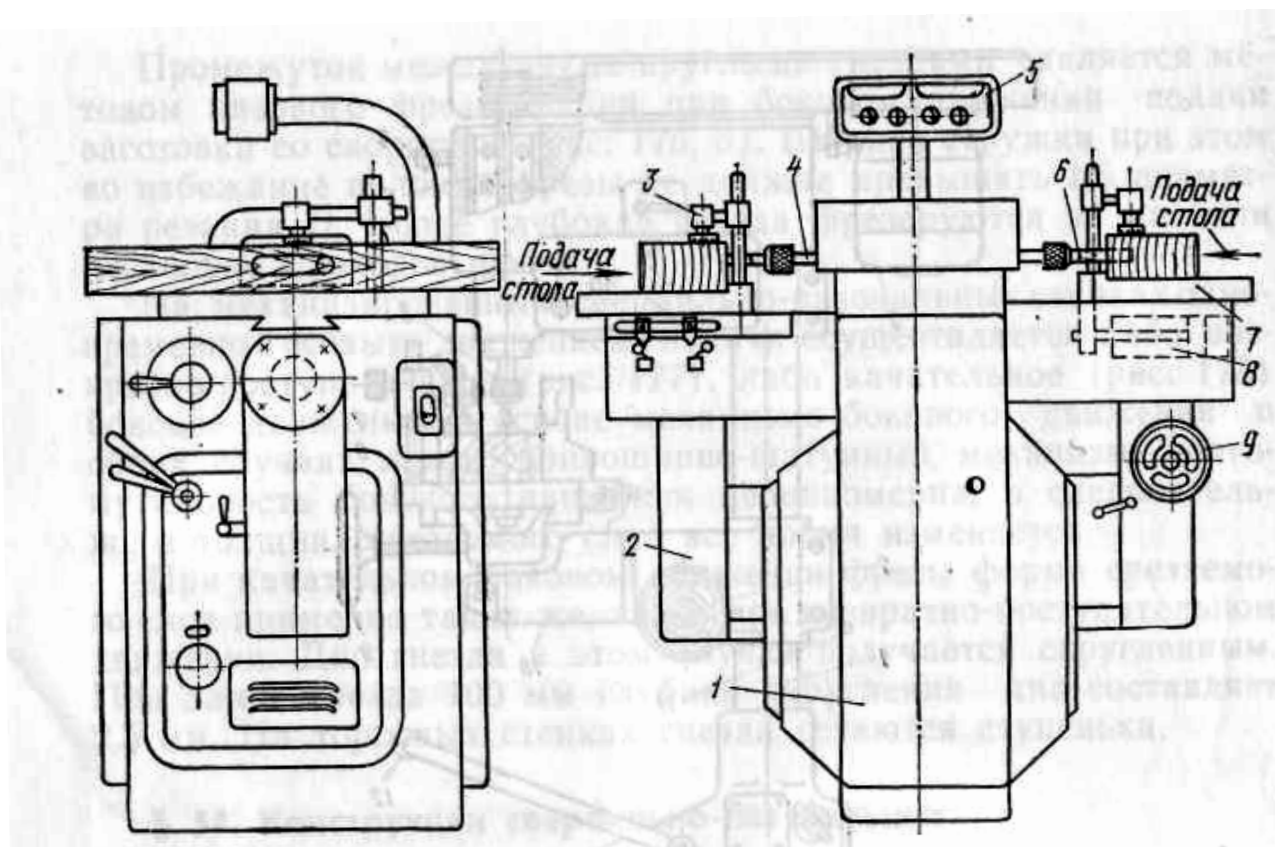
Сверлильно-пазовальный горизонтальный станок СВПГ-2:
